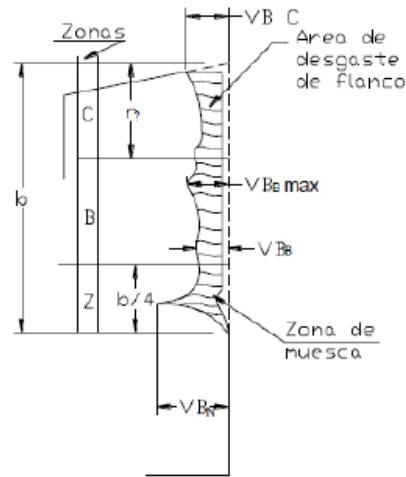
20 Zonas de desgaste en el flanco de la herramienta de corte [9]
